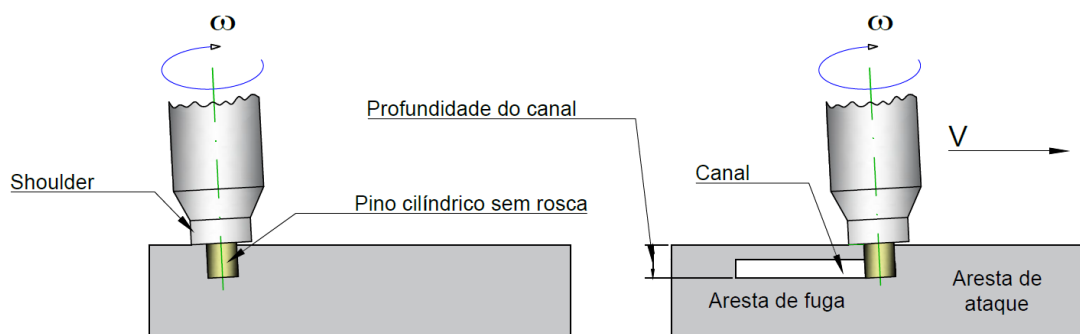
Representação do MFSC - *Modified Friction Stir Channeling* com pino cilíndrico sem rosca, adaptado de [23].
